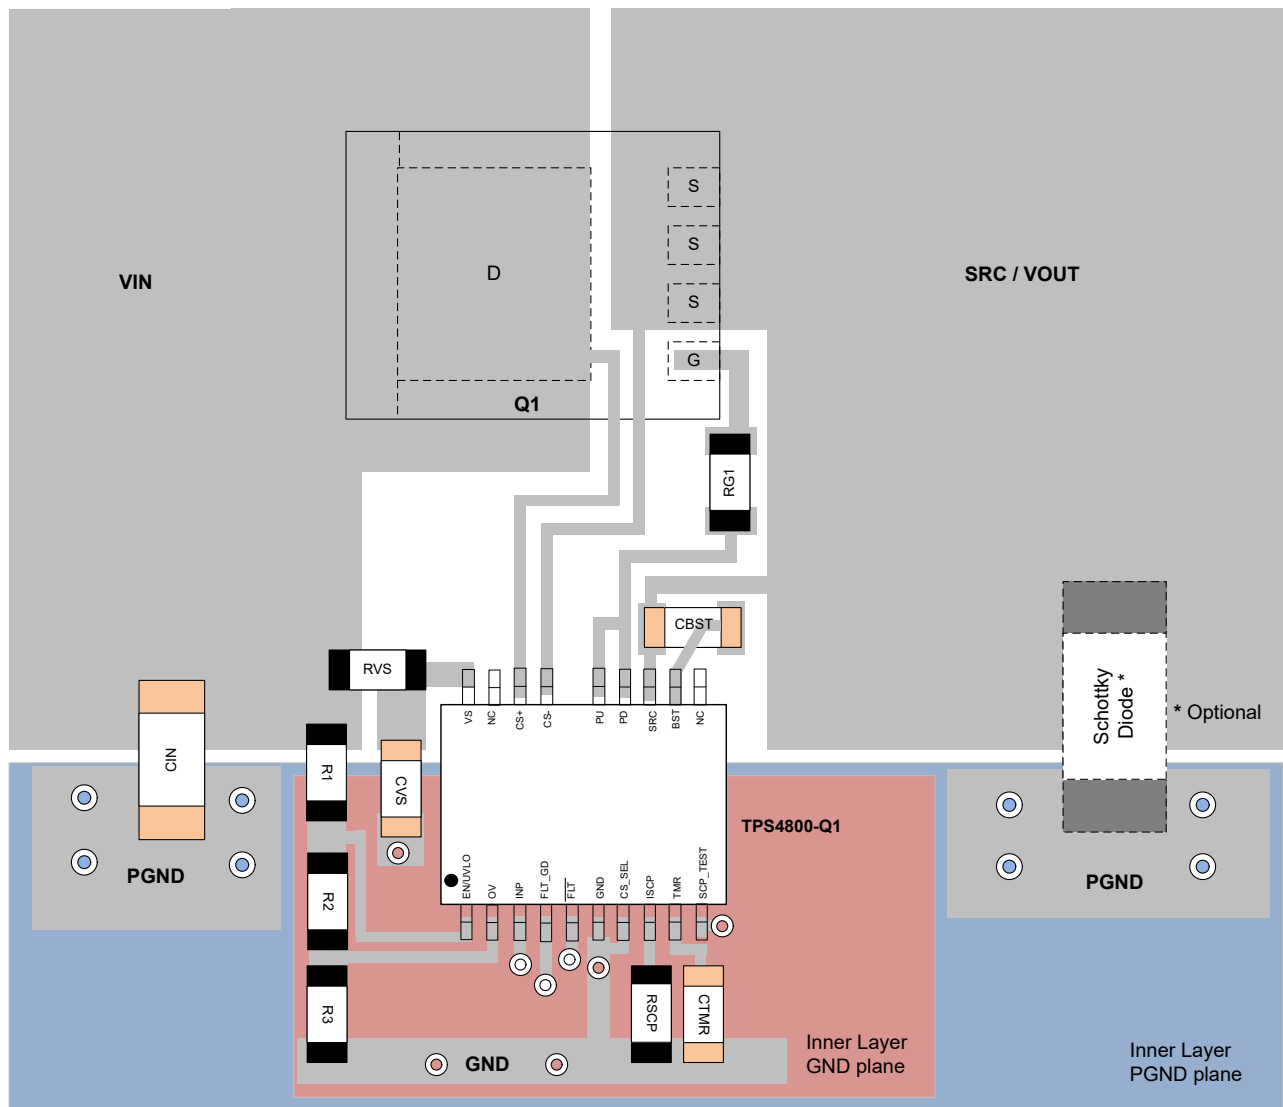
具有基于 VDS 电流检测的 TPS4800-Q1 典型 PCB 布局示例
